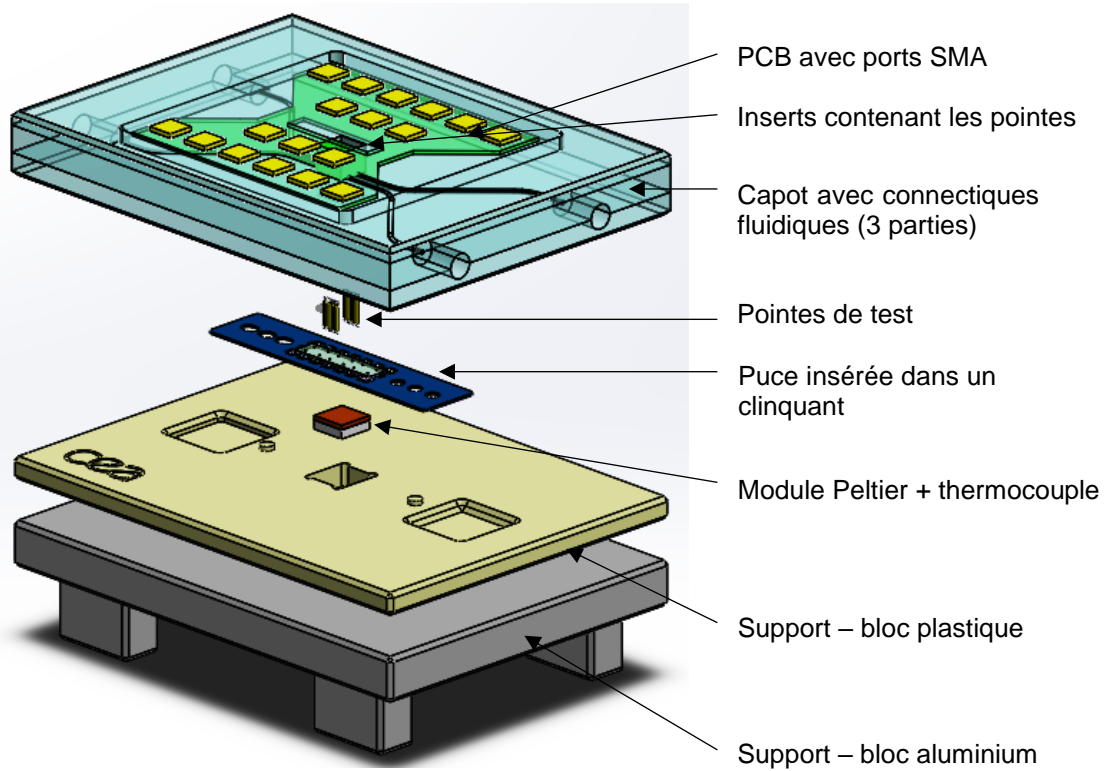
Vue éclatée de la plateforme comportant le bloc fluidique en face avant (version A).
